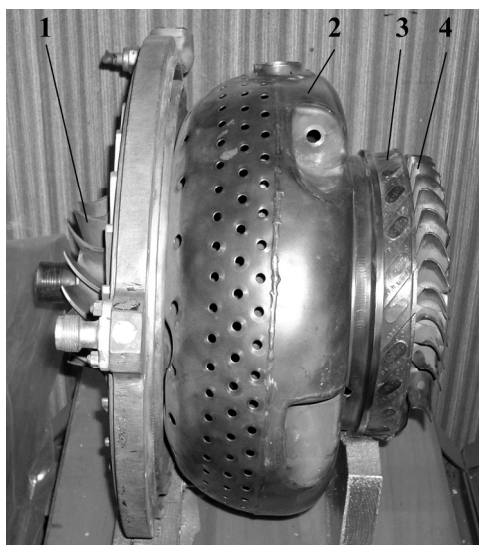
Учебный стенд-макет: газотурбинный двигатель ГТД-16М:
